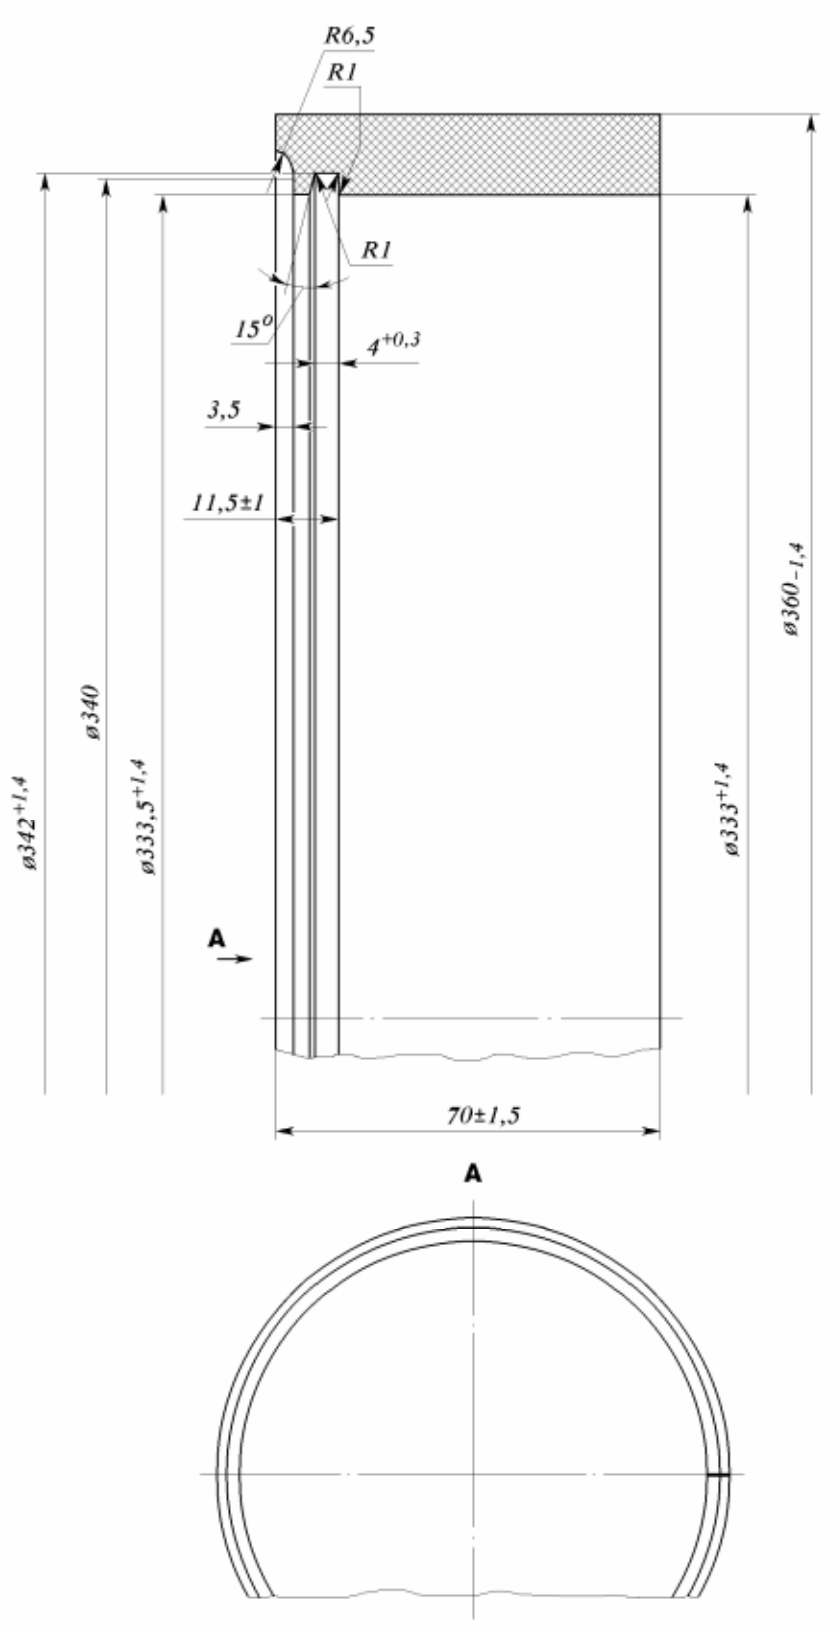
Кольцо монтажное для установки торцевого уплотнения (76.90 Н- 28А4)
